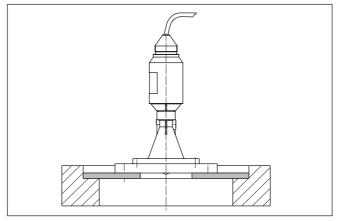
Montagem com um flange adaptador, por exemplo, na tampa de um poço.
